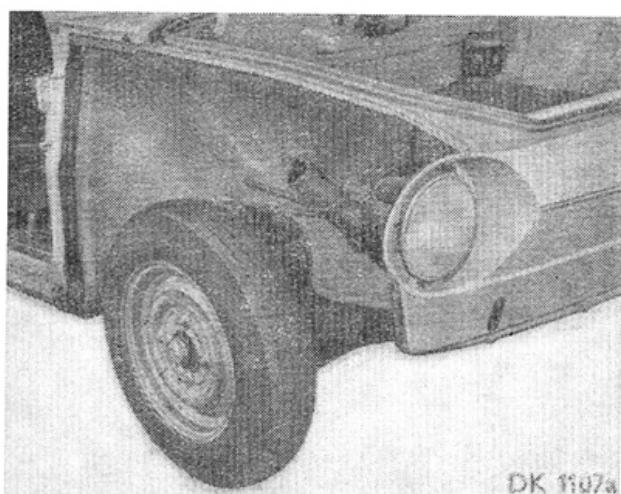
/1 Rukojeť uzávěru přední kapoty – přístup k upevňovacímu šroubu táhla
